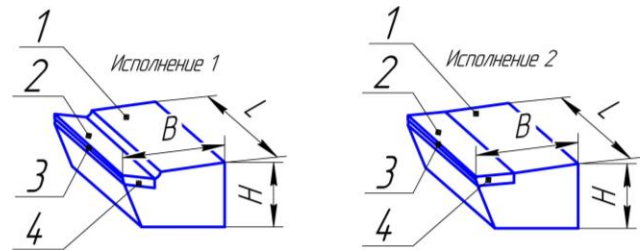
Конструктивные и геометрические параметры токарного проходного безвершинного сабельного резца (в диметрии)
